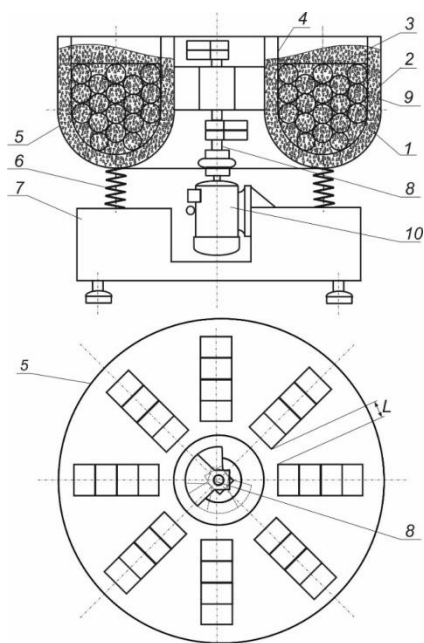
Схема пристрою для вібраційної обробки внутрішніх поверхонь деталей прохідного типу
